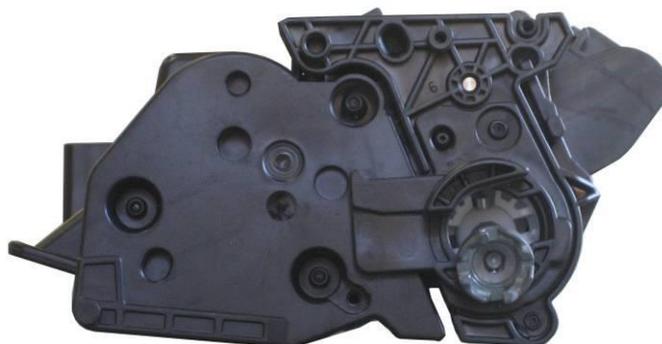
2 - Detalhe da engrenagem do OPC.
